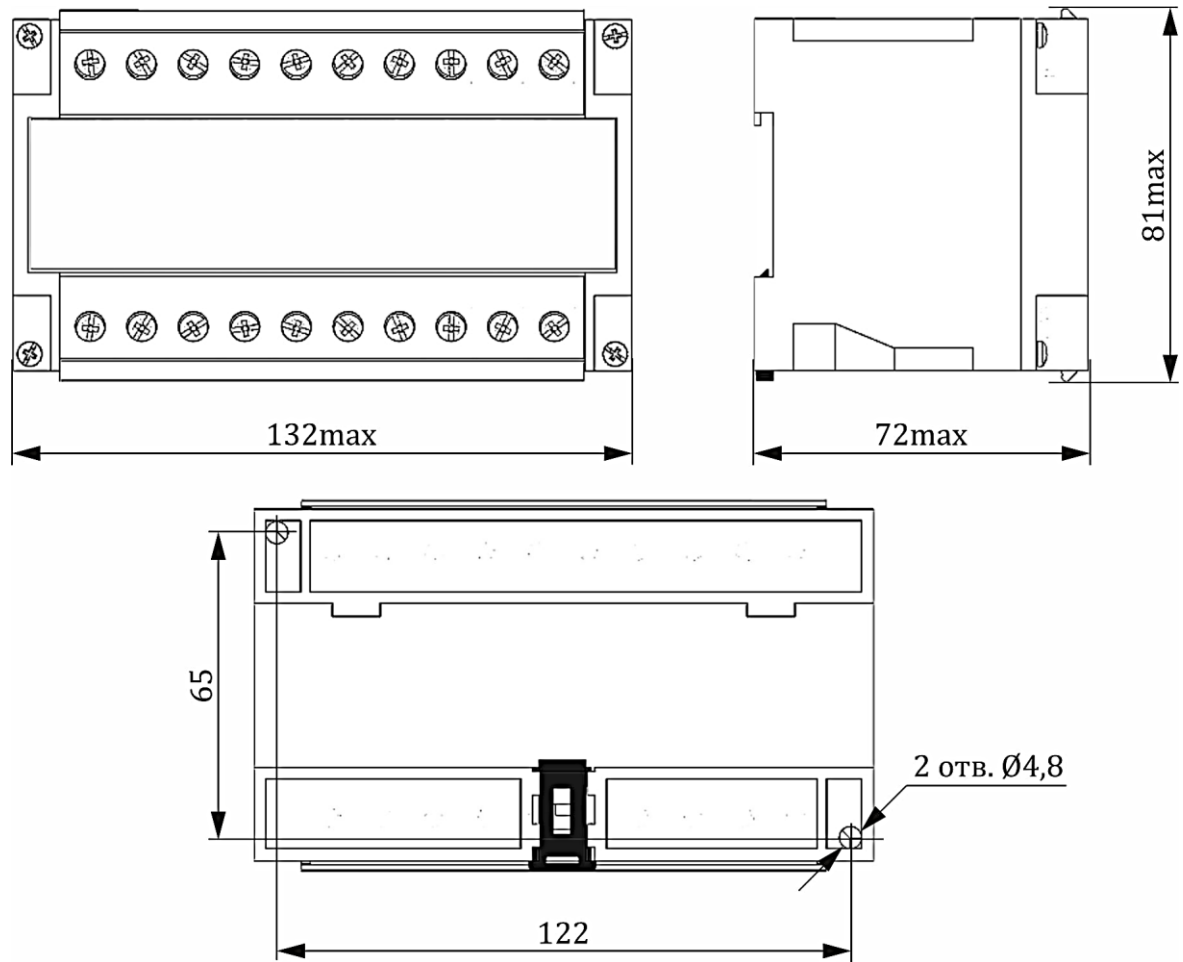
Габаритные и установочные размеры корпуса М20
